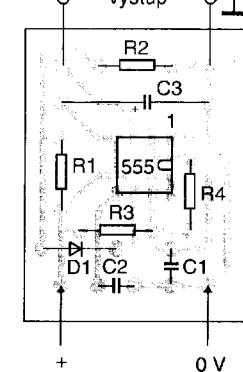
Deska s plošnými spoji C318 pro zapojení z obr. 37 a deska, osazená součástkami
